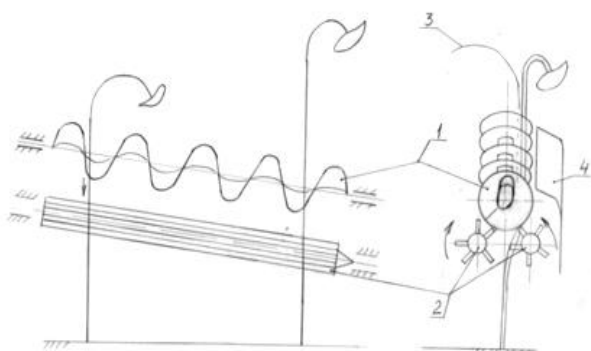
Схема подающего шнекового устройства с дополнительными протягивающими вальцами:
